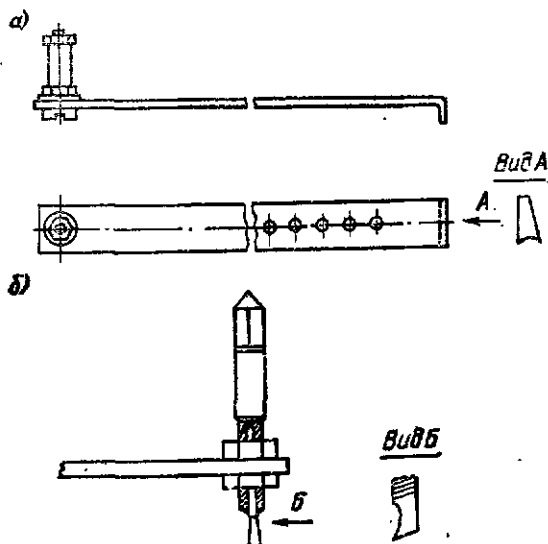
Резак для прорезания круглых отверстий, выполненный из ножовочного полотна (а) и из метчика (б)
